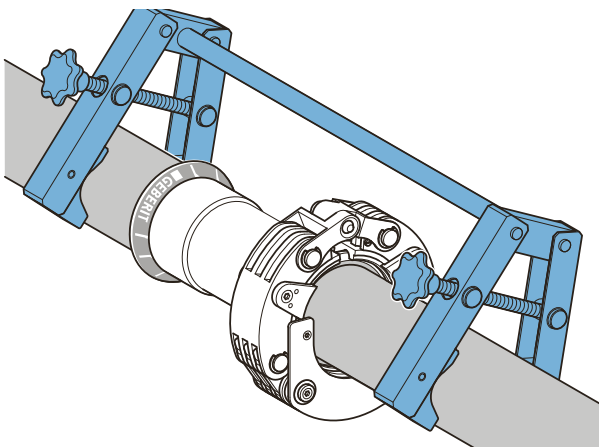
Rohr und Fitting mit Montagehilfe fixiert
